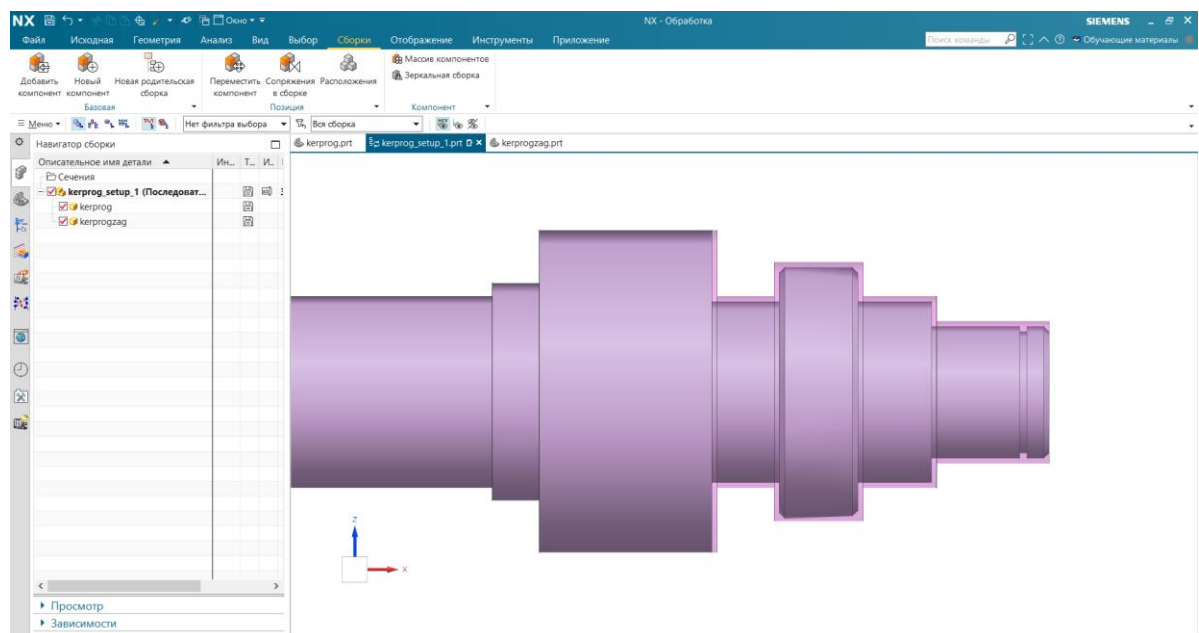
Поєднання зображення деталі та заготовки в системі NX CAM
